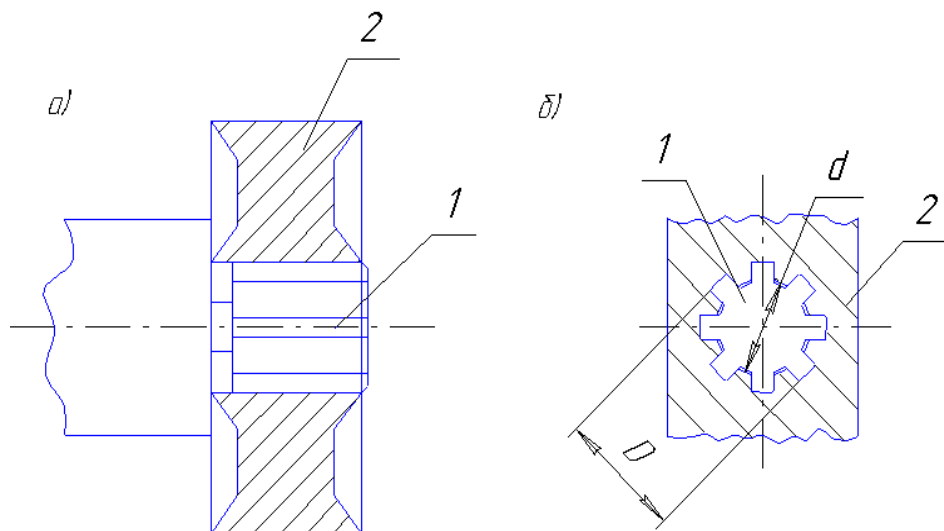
а) шлицевое соединение; б) центрирование по наружному диаметру 1-шлицевой вал; 2- шлицевая втулка (зубчатое колесо, маховик).
